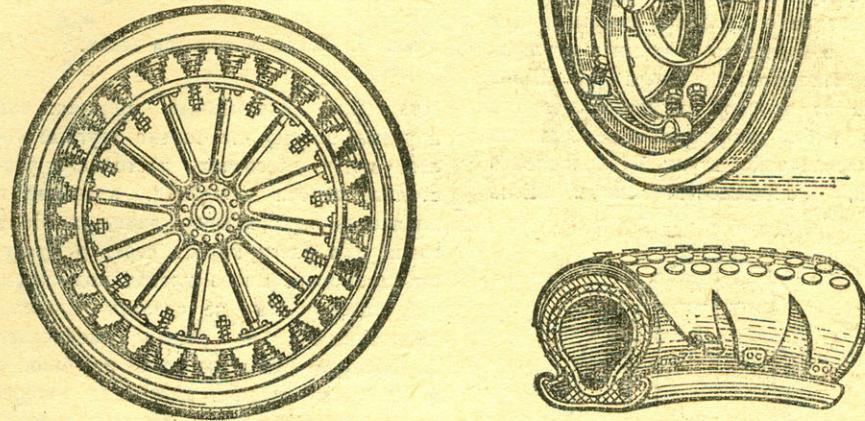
Пружинные колеса и шина из пружин в кожаном чехле.
